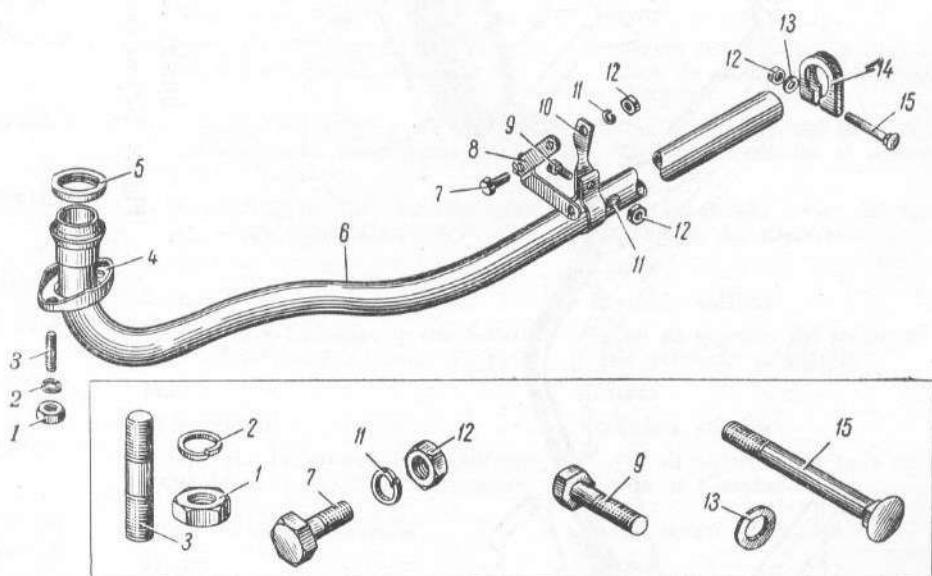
Aufnahmerohr des Schalldämpfers mit Aufhängung
